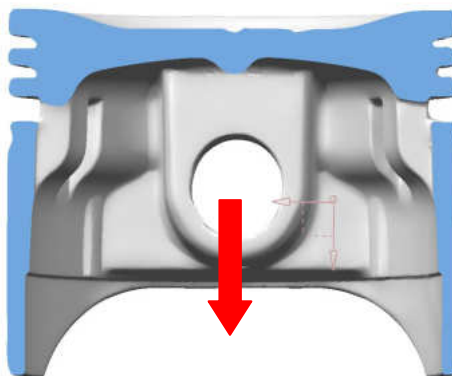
Vista em corte do pistão com direção de desmoldagem.
